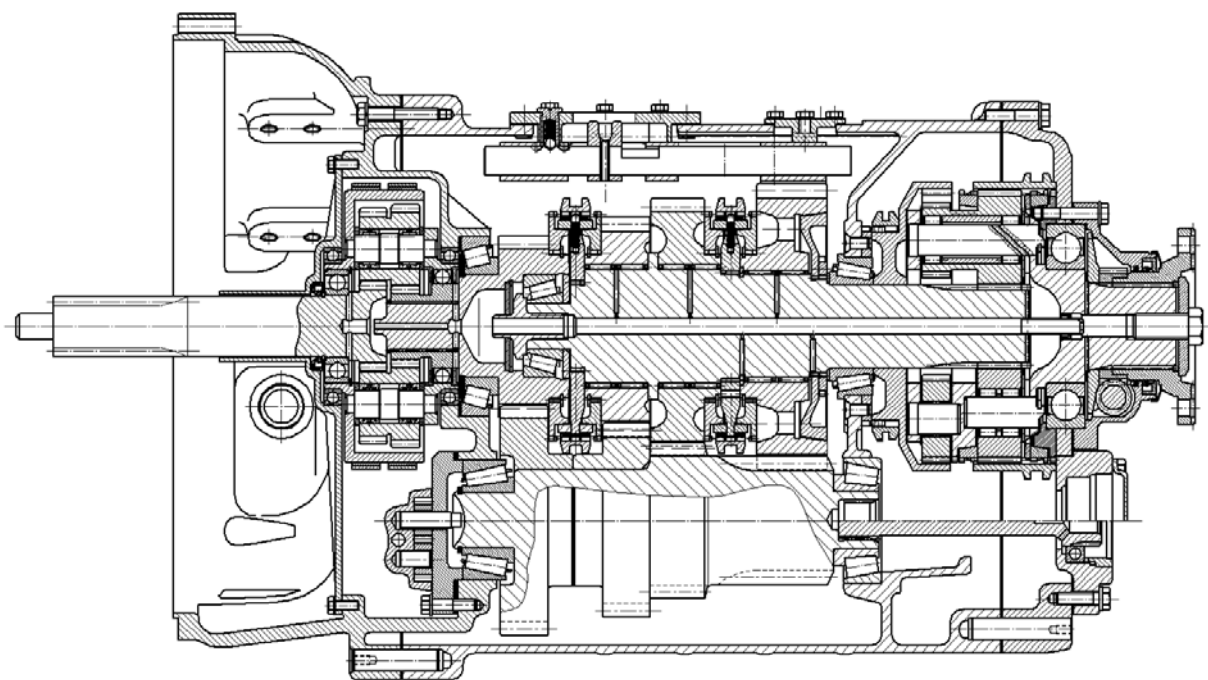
Шестнадцатиступенчатая коробка перемены передач
